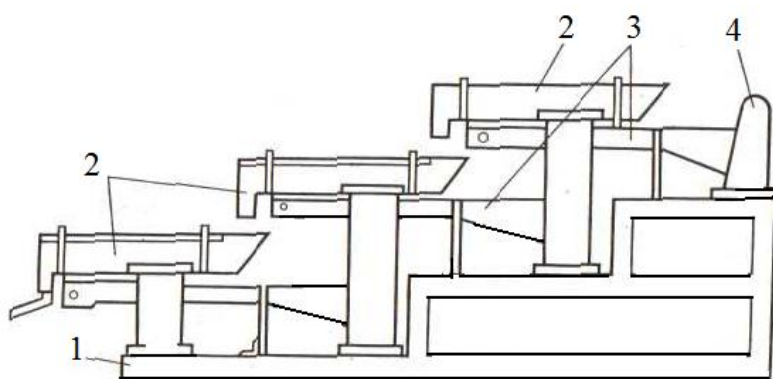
Ферромагнитная обогатительная установка ФОУ-2
